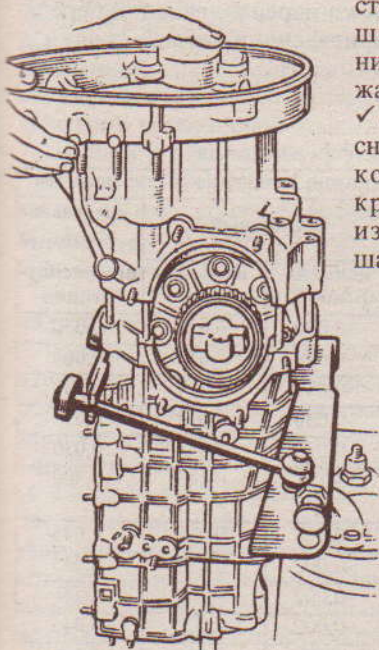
Коробка передач в приспособлении для сборки и разборки
